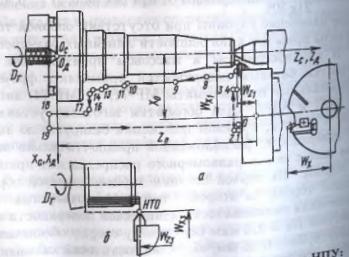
Схема обтачивания вала на станке с ЧПУ: а – чистовой проход; б – нарезание резьбы
